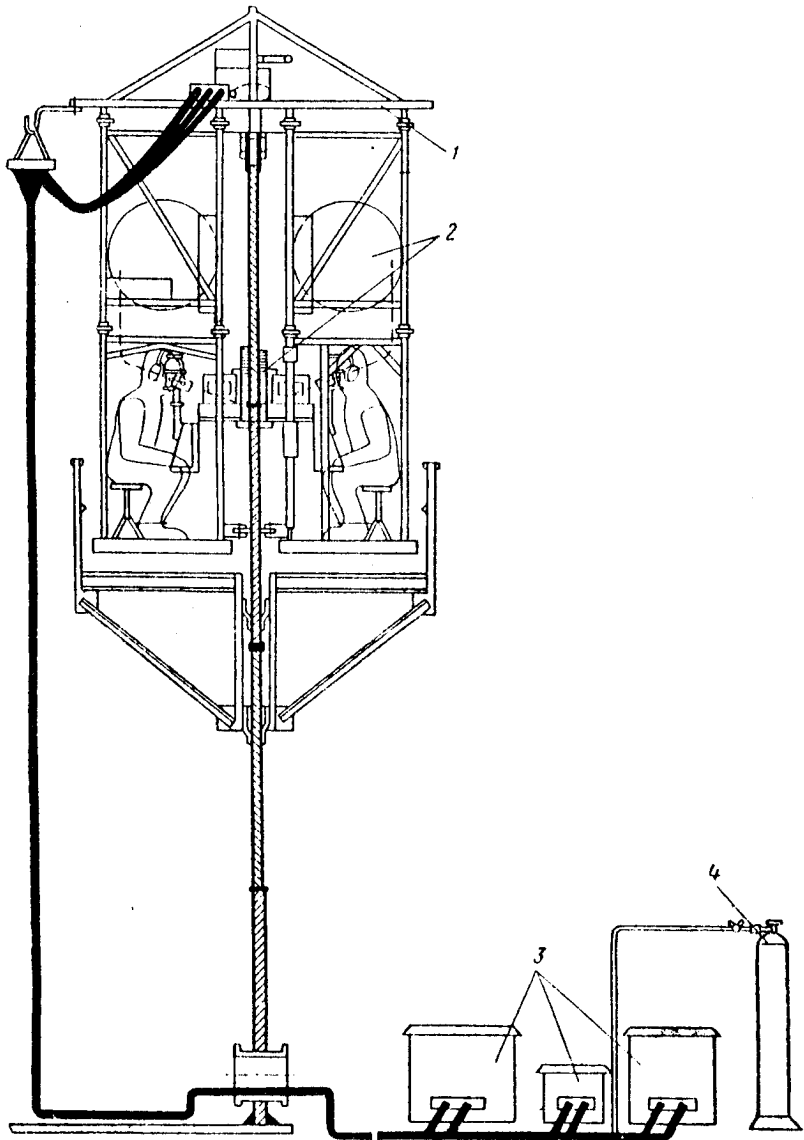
Автоматична установка для зварювання горизонтальних стиків стінки резервуара з напівпримусовим формуванням шва:
